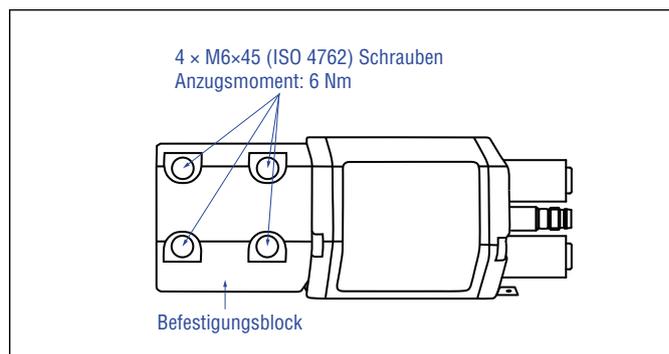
Befestigung des RDV Sensorelektronikgehäuses (Beispiel Bodenanschluss)
